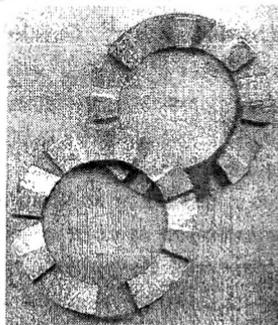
Изделия с кулачками, обработанные по схеме с непрерывным процессом деления
